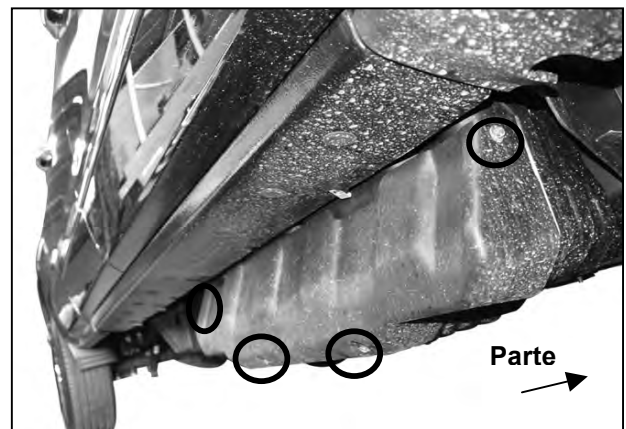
Ilustración de soporte frontal izquierdo/del lado del conductor conectado al estribo
